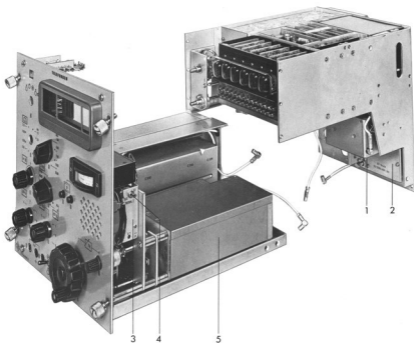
KW-Empfänger E 724 KW/2 - Einschub getrennt in zwei Baugruppen: "Frontrahmen" (links) und "Oberes Chassis" (rechts)
